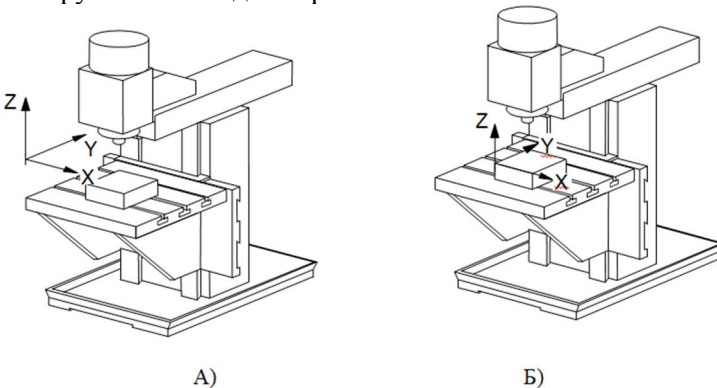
Системи координат верстата (А) і заготовки (Б)
